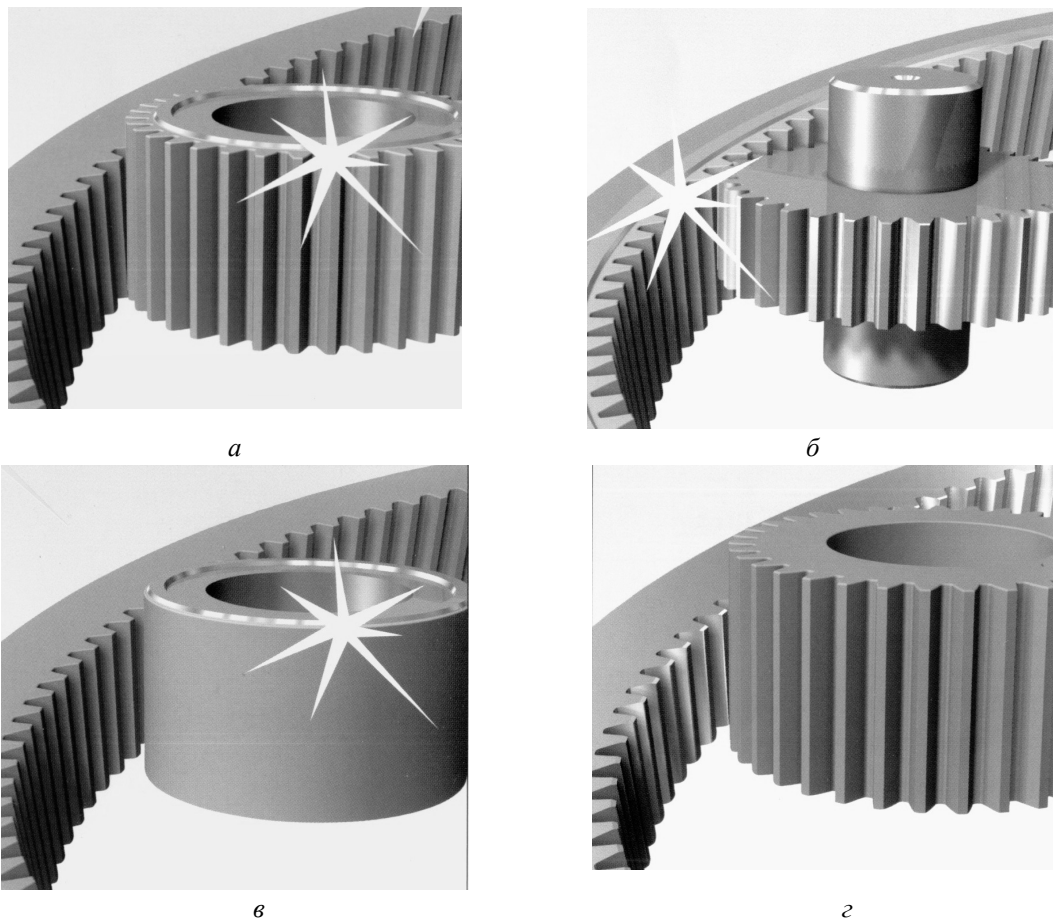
Схема двопрофільного безззорного хонінгування зубців з реверсом обертового руху та радіальною подачею на верстаті з ЧПК мод. К-300: а – правлення хону алмазним інструментом; б – чорнове оброблення зубчастого колеса збірним інструментом із алмазним вінцем; в – правлення хону за діаметром головок зубців алмазним кругом; г – чистове оброблення зубчастого колеса спеціальним хонінгувальним інструментом
